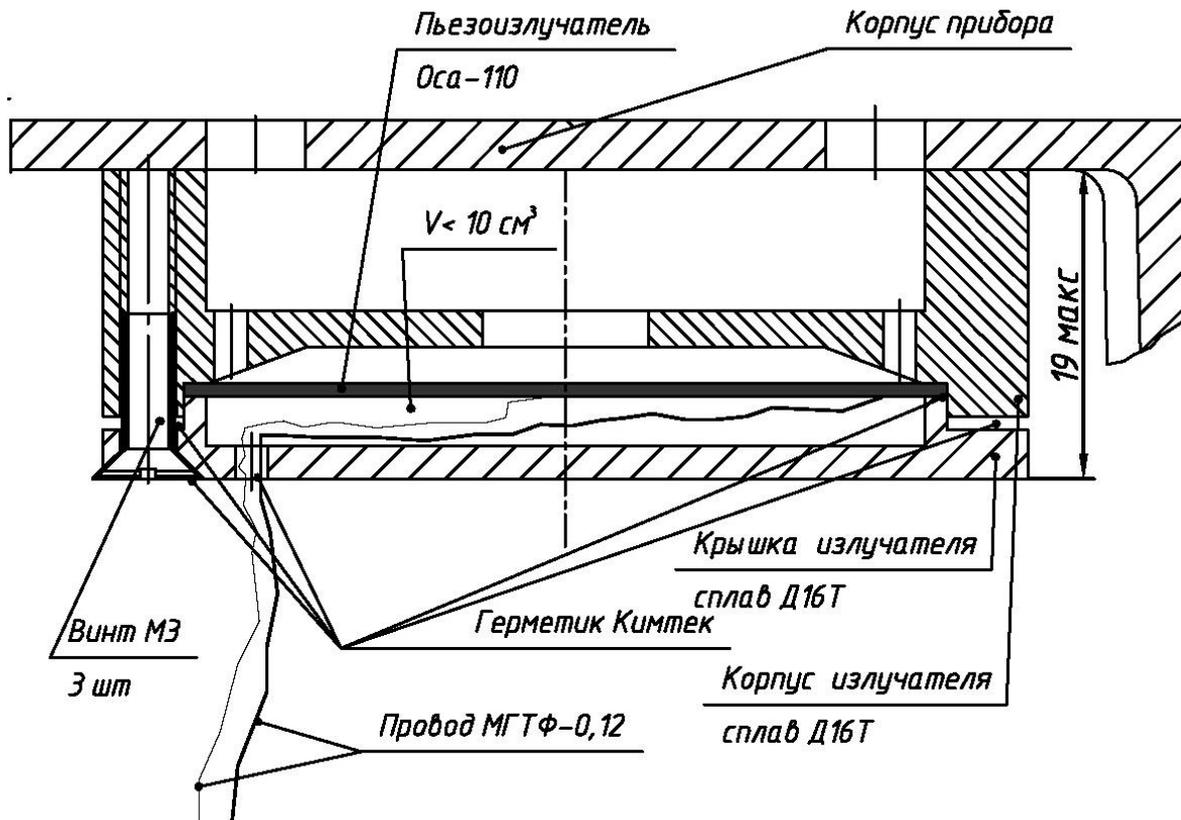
Рисунок звукового излучателя для оповещателей Филин-1 и Филин-2
